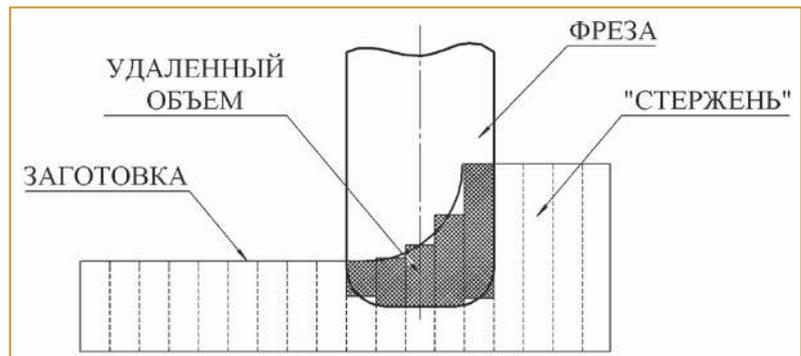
Схема разбиения модели заготовки на стержни по одной из осей станочной системы координат и вычисление объема материала, снимаемого фрезой
